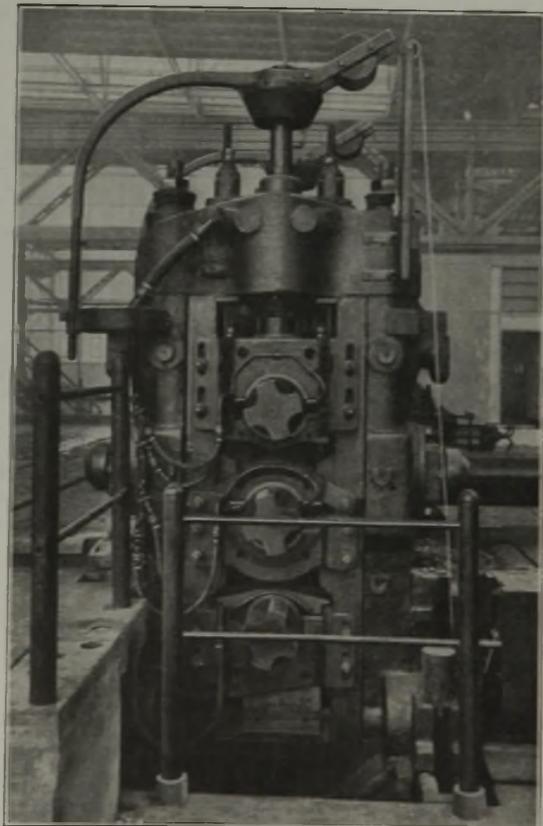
550er Trioerüst. Einbaustücke ausgerüstet mit formgepreßten halbrunden Lagerschalen aus Kunstharz-Preßstoff.
